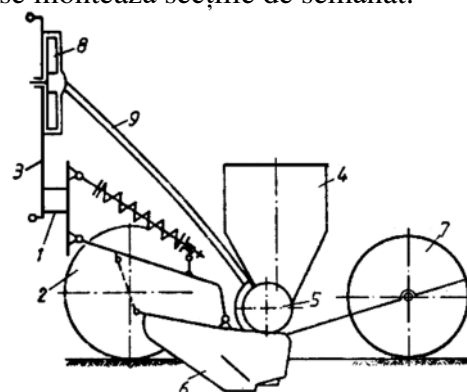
Schema constructivă a unei mașini pentru semănat plante prășitoare:
